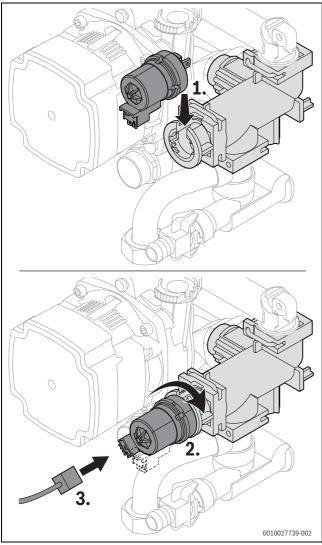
Montare il motore sulla valvola a 3 vie (variante senza viti)
